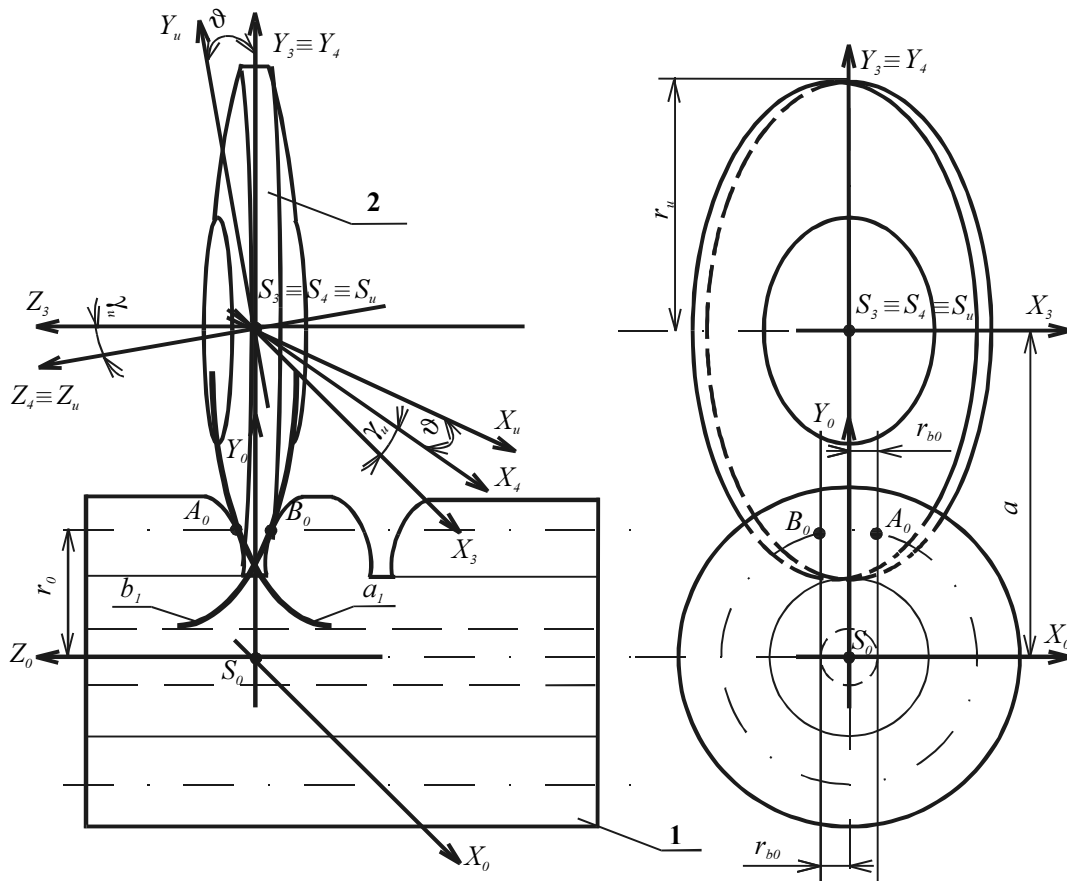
Схема утворення виробної поверхні дискового інструмента [2]
